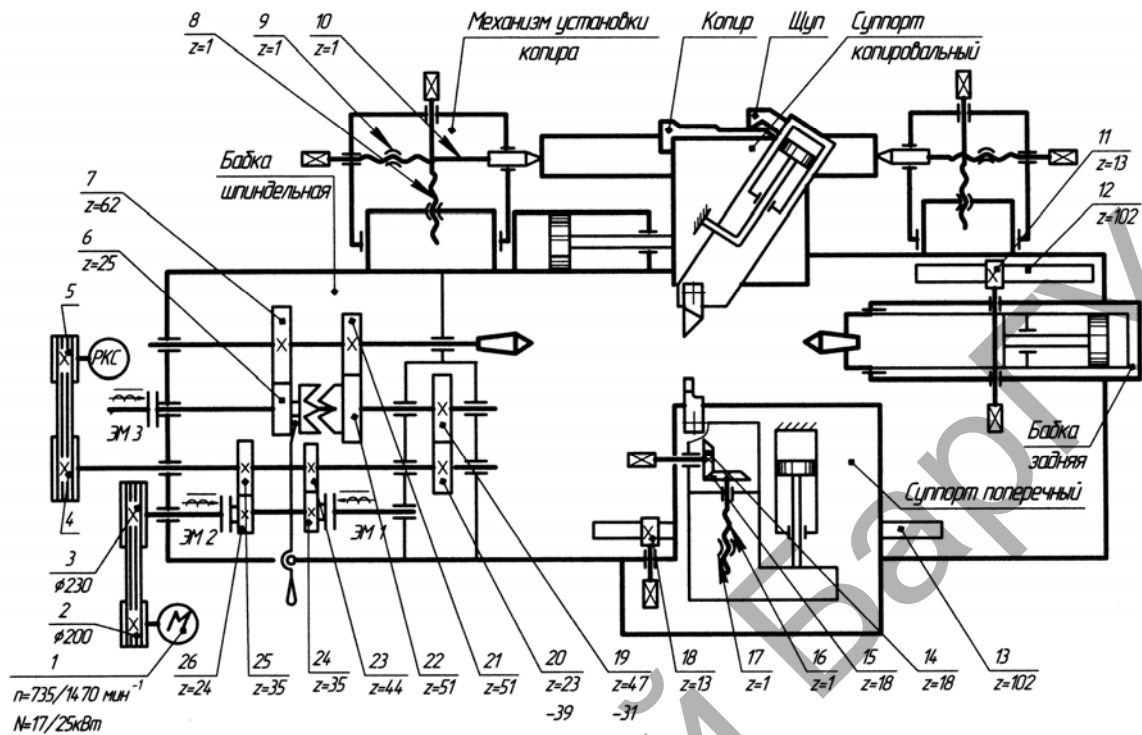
Кинематическая схема станка модели EM473-1-02A
